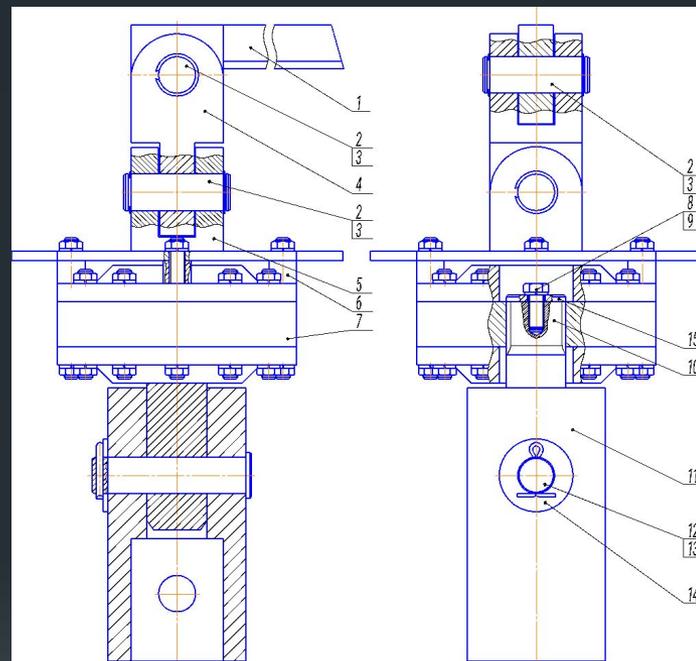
Вращатель: 1 – верхний крепеж; 2 – ось; 3 – стопорное кольцо; 4 – ось; 5 – нижний крепеж; 6 – втулка; 7 – гидромотор; 8,9 – болтовой крепеж; 10 – вал; 11 – переходник; 12 – палец; 13 – шплинт; 14 – шайба
